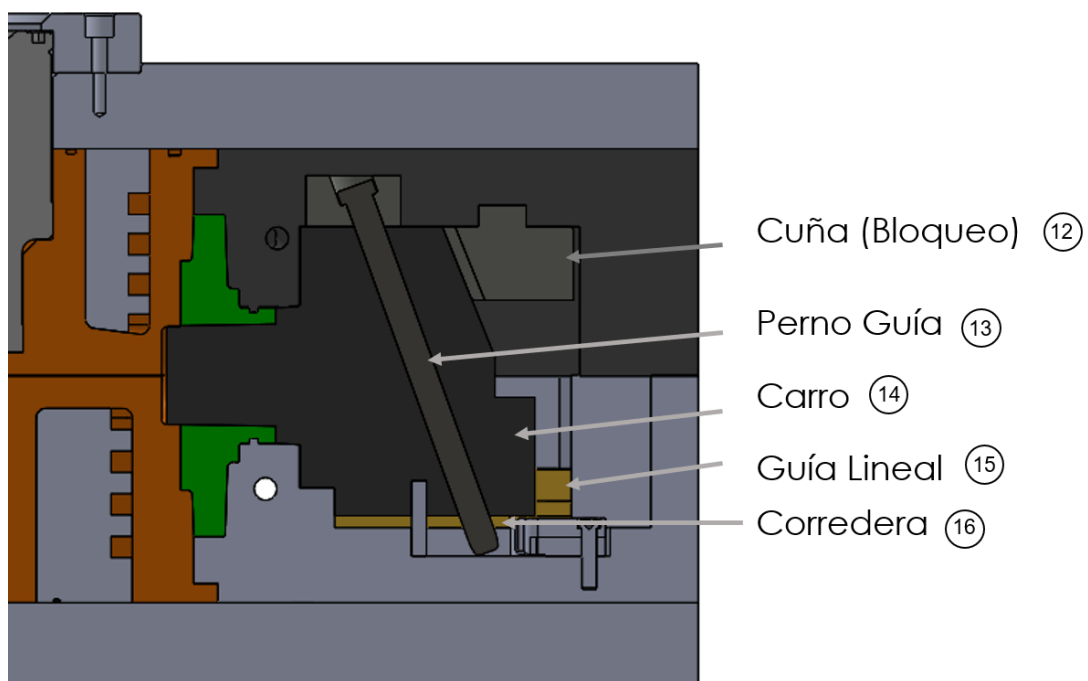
Sistema de Moldeo y Liberación Mecánico, Molde Cerrado.
